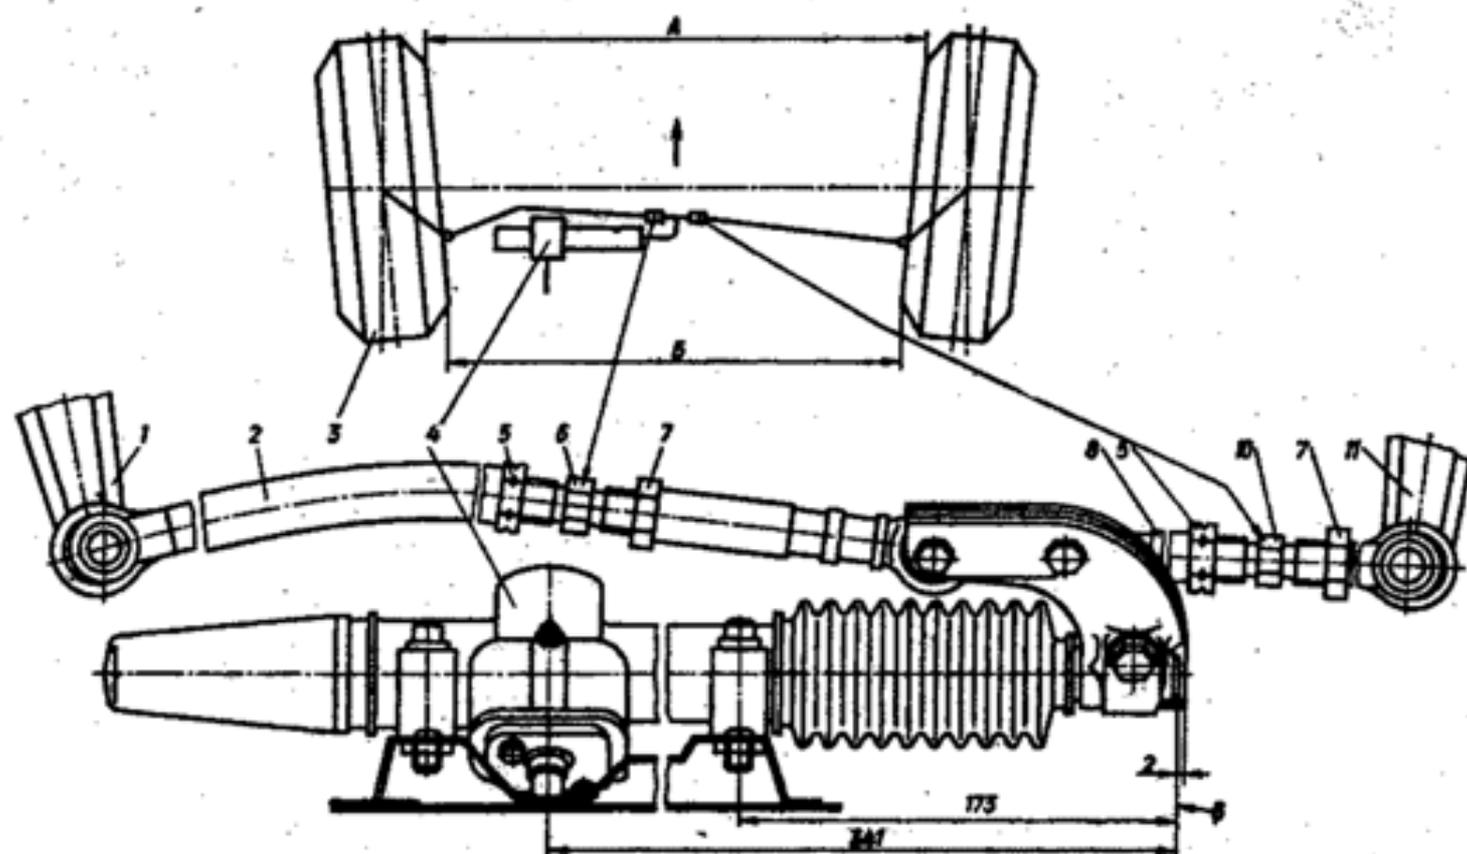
Привод рулевого управления: 1 - рычаг поворотный левый; 2 - левая рулевая тяга в сборе; 3 - колесо передней подвески левое; 4 - механизм рулевой; 5 - левая контргайка; 6 - стяжка левая; 7 - правая контргайка; 8 - правая рулевая тяга; 9 - колесо передней подвески правое; 10 - стяжка правая; 11 - рычаг поворотный правый; А - размер спереди между шинами; Б - размер сзади между шинами; В - положение рейки соответствующее прямолинейному движению автомобиля
